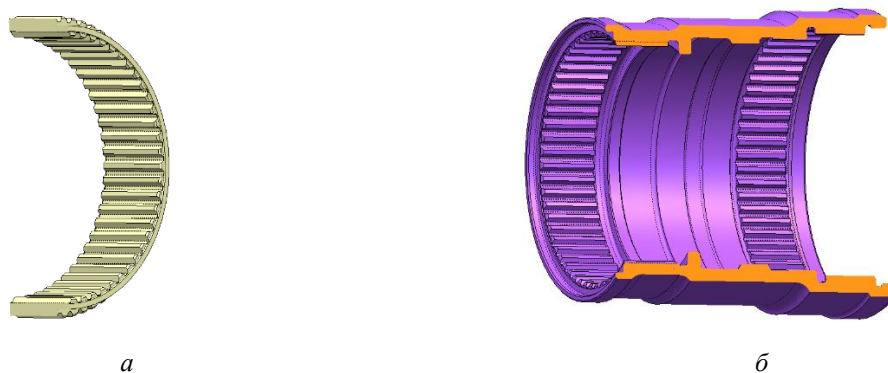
3D-модели деталей: *а* – втулка шлицевая; *б* – вал привода КВД
